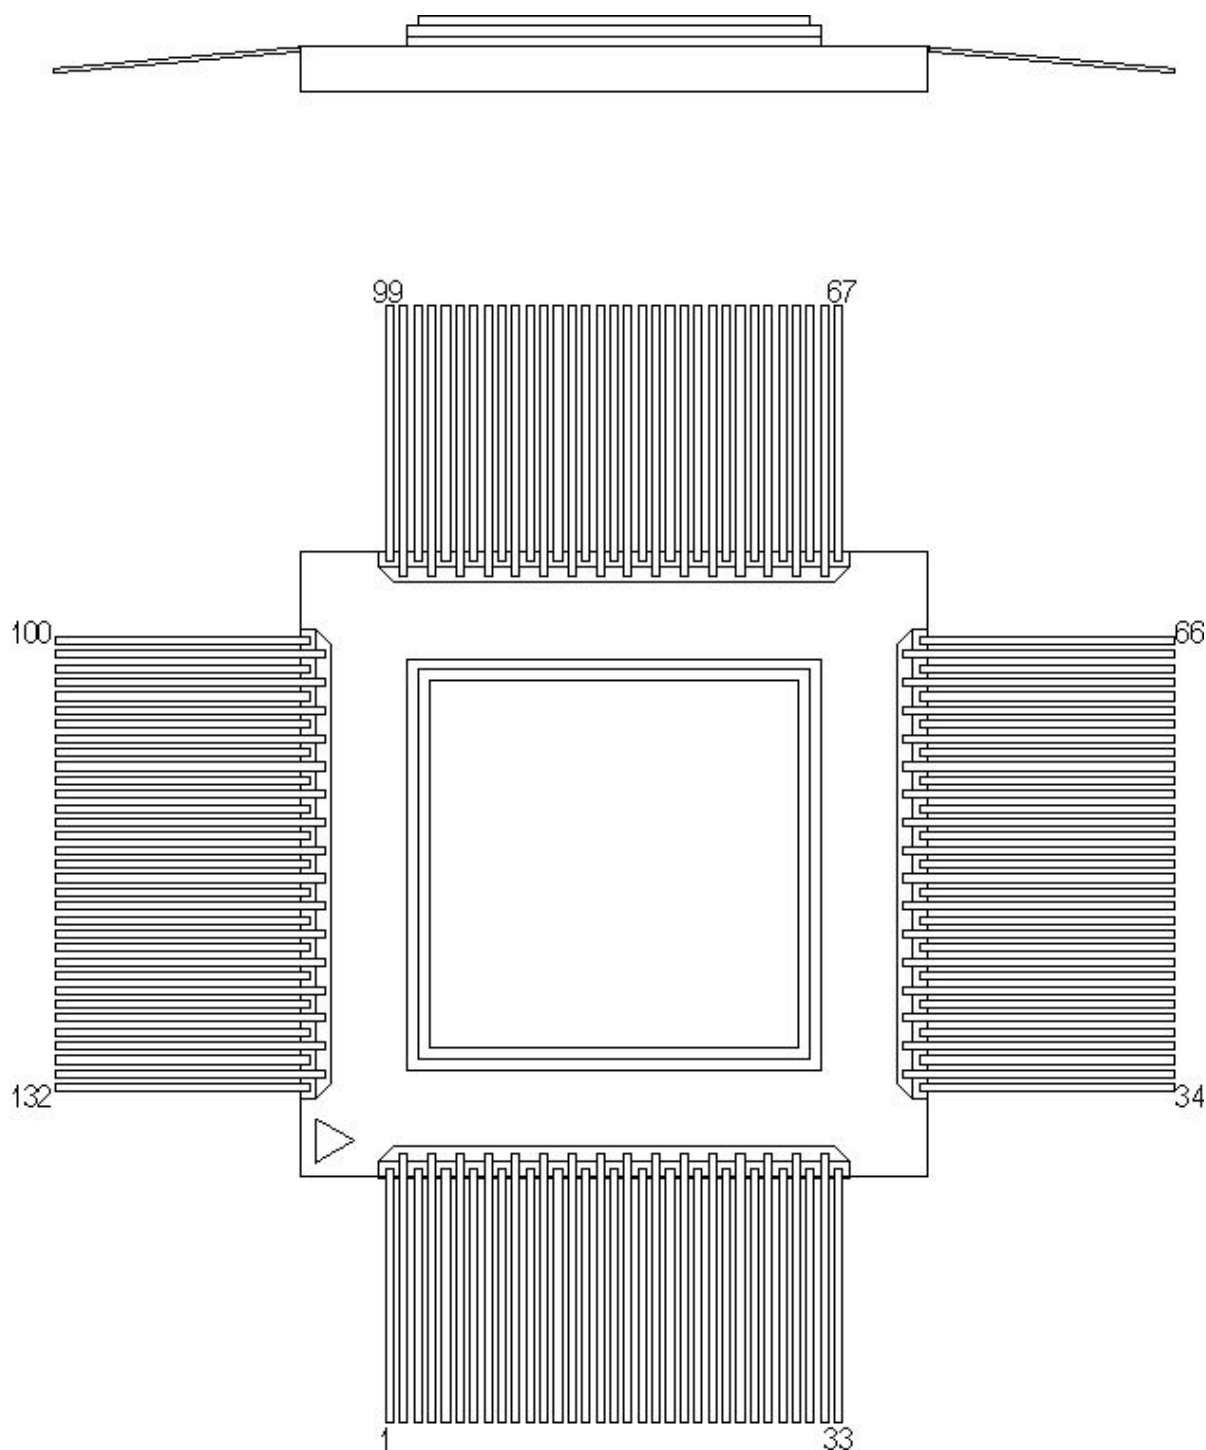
Внешний вид корпуса 4229.132-3
